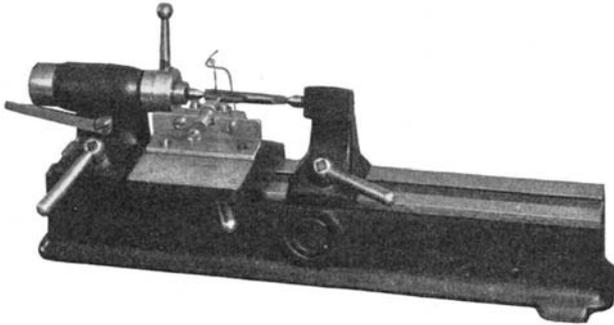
Einrichtung einer Durchmesserprüfung dreinutiger Gewindebohrer (AEG).
